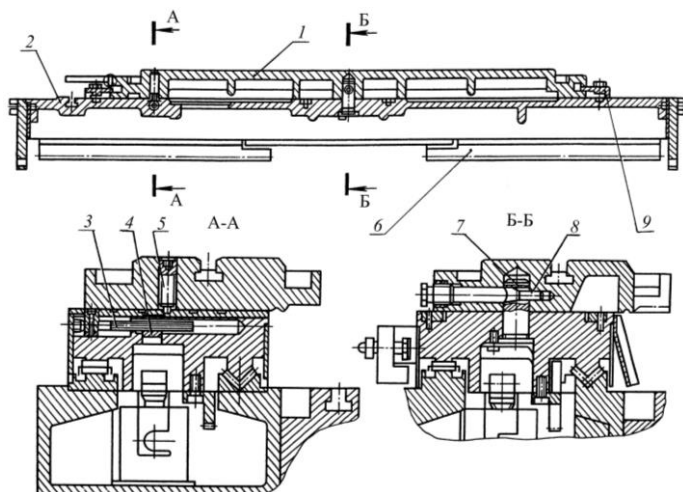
Стол универсально-заточного станка модели 3Д642Е
